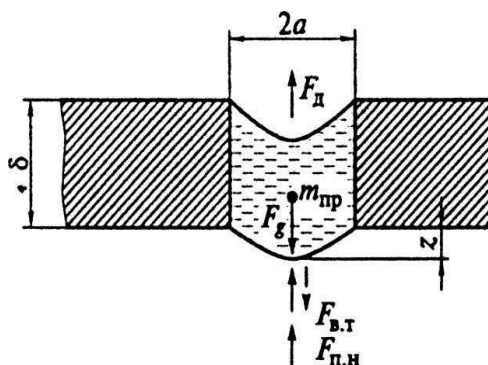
Сферическая модель сварочной ванны: F_d – сила давления дуги; F_g – сила тяжести сварочной ванны; $F_{в.т}$ – силы вязкого трения при колебании ванны; $F_{п.н}$ – силы поверхностного натяжения с наружной и внутренней поверхности сварочной ванны; a – полуширина сварочной ванны; $m_{пр}$ – приведенная масса сварочной ванны; δ – толщина свариваемого металла; z – провисание сварочной ванны [Spherical welding pool model: F_d – arc pressure force; F_g – gravity of the welding pool; $F_{в.т}$ – viscous friction force when the bath oscillates; $F_{п.н}$ – surface tension forces from the outer and inner surfaces of the welding pool; a – half-width of the primary bath; $m_{пр}$ – reduced mass of the welding pool; δ – thickness of the metal being welded; z – sagging welding pool]
